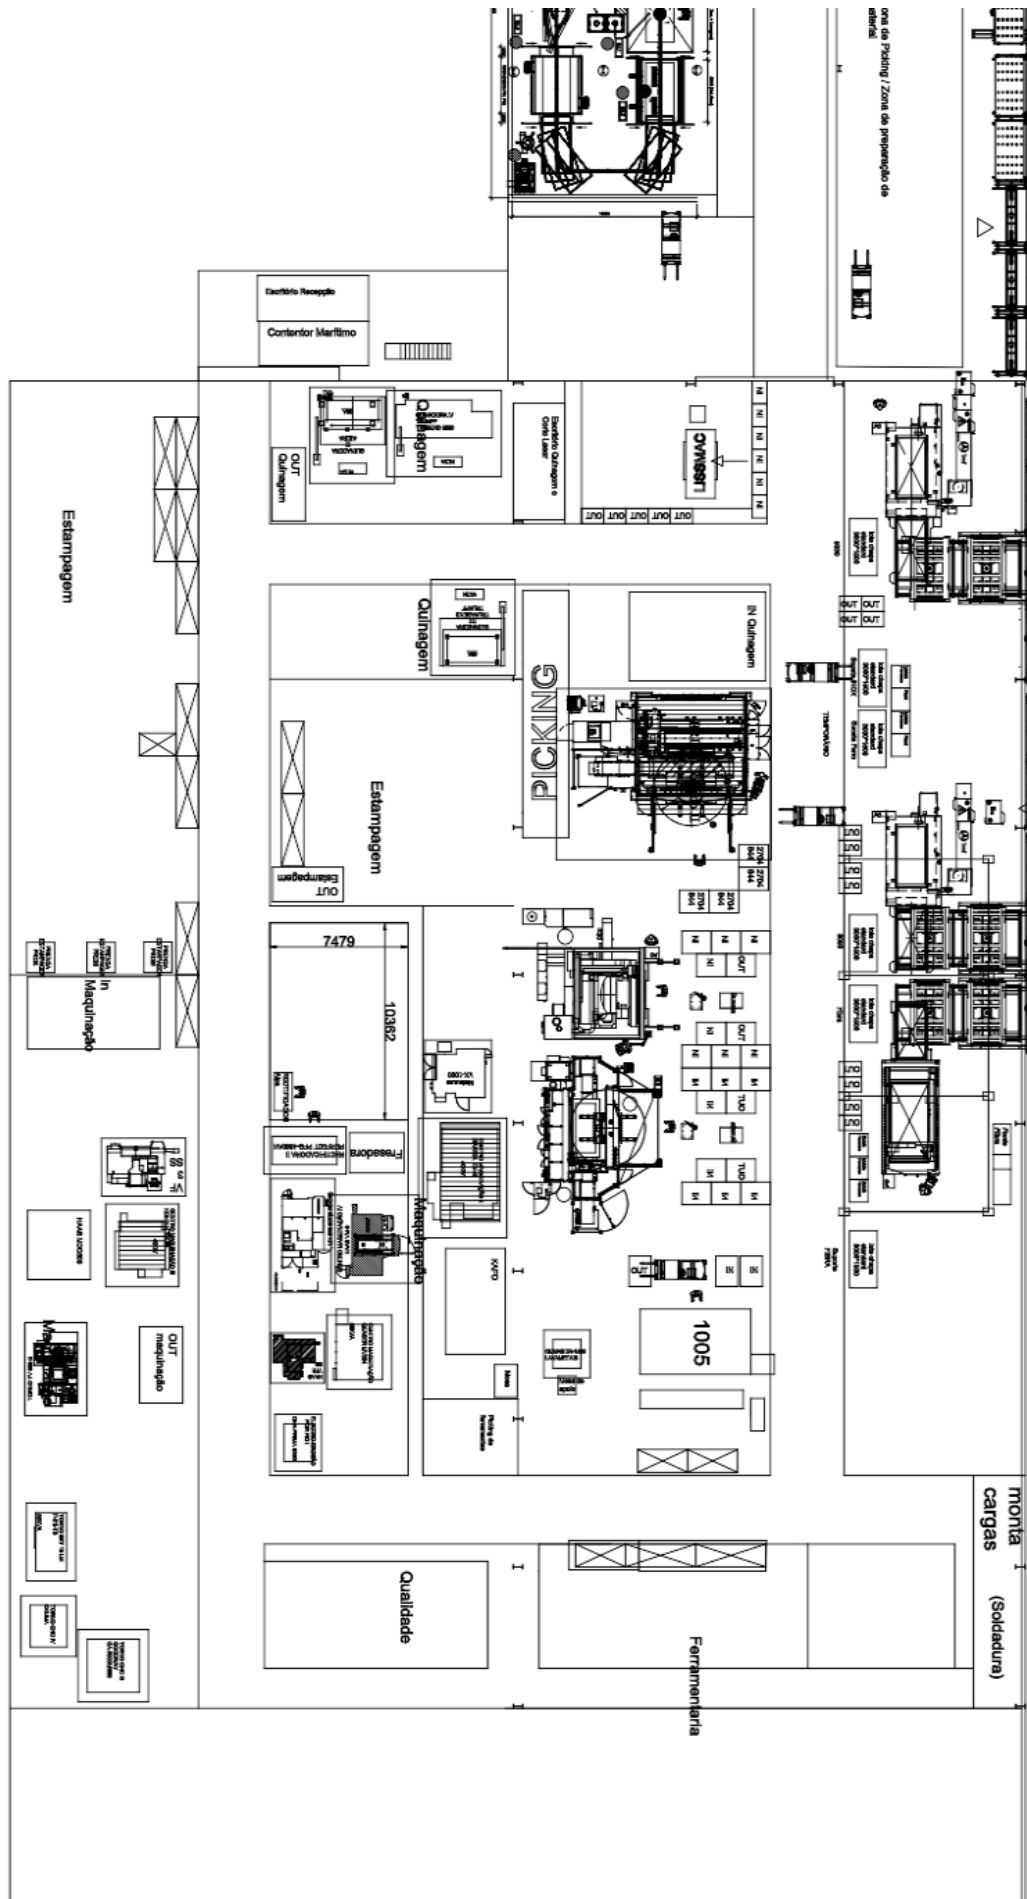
Planta do Pavilhão 1 do Chão de Fábrica
